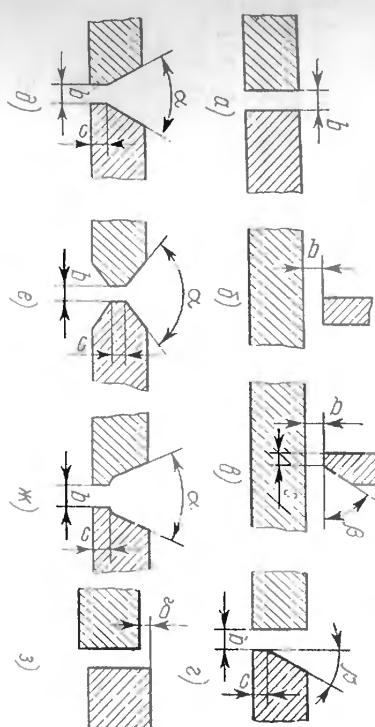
Конструктивные элементы кромок, подготовленных под сварку под сварку заготовок и сборку последних под сварку:
